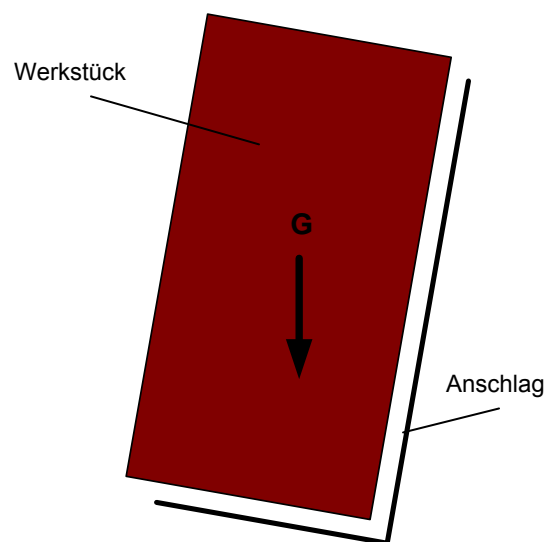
Ausrichten der Werkstücke durch Gewichtskraft
